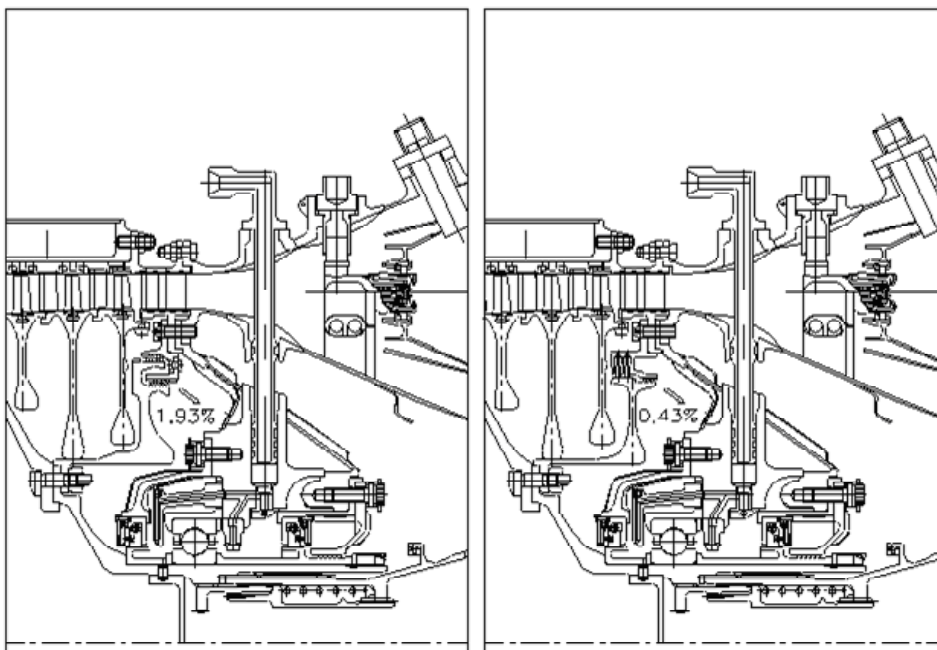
Лабиринтные и ЩУ в компрессоре двигателя ТВ3-117ВМА-СБМ1(СБМ1В)
